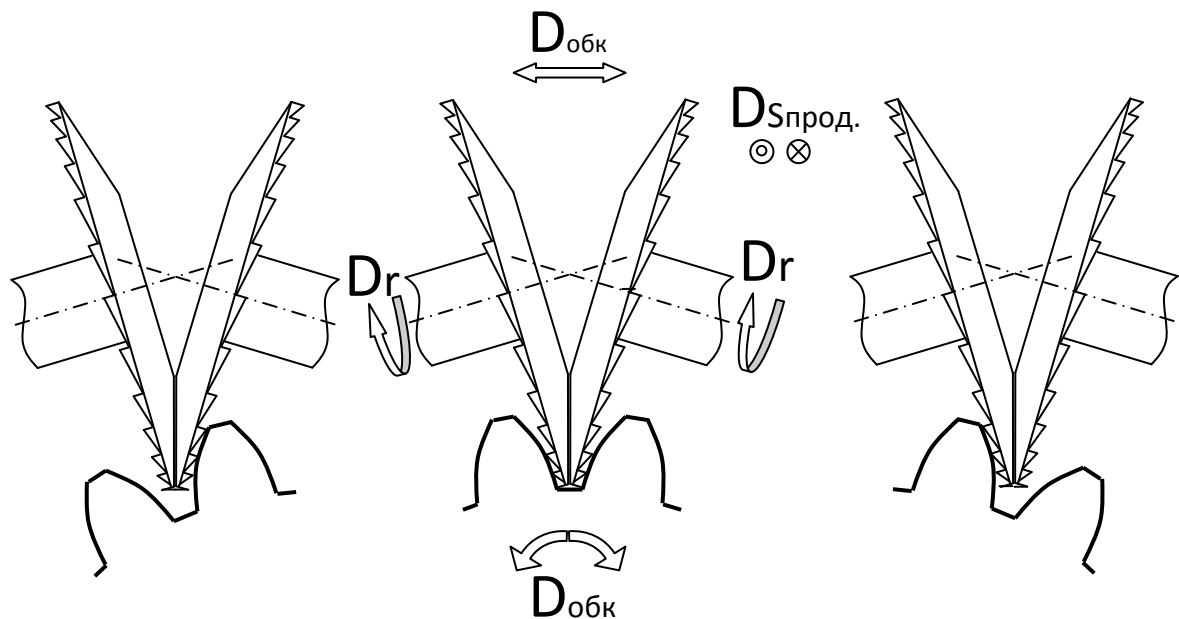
Кинематика формообразующих движений при нарезании прямозубых цилиндрических колес парой специальных торцовых фрез
